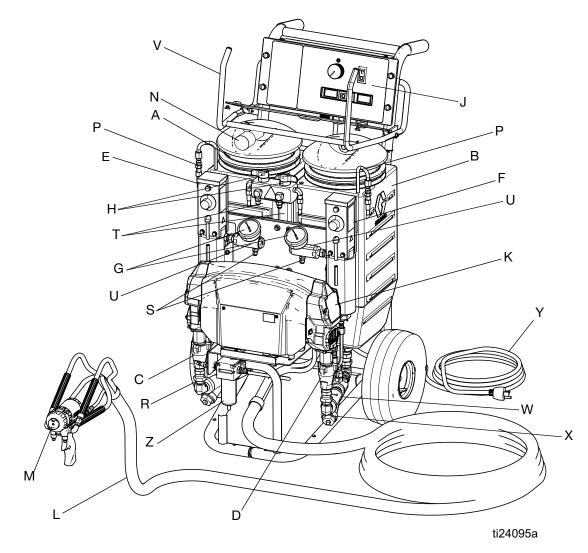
Identificación de los componentes, sistemas con calentador (ref. pieza AP9572 representada)
